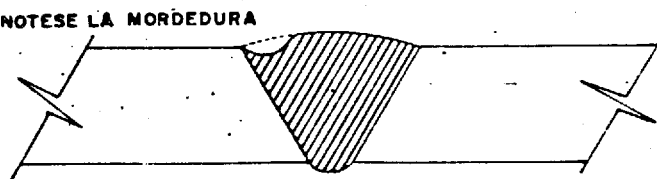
CONDICION DE MORDEDURA (REE AWS WELDING HANDBOOK) (Ref. 7)
